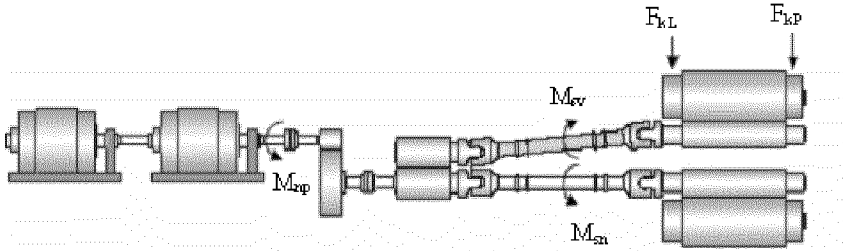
Схема главного привода клетки кварто широкополосного стана горячей прокатки с шестеренчатой келью
